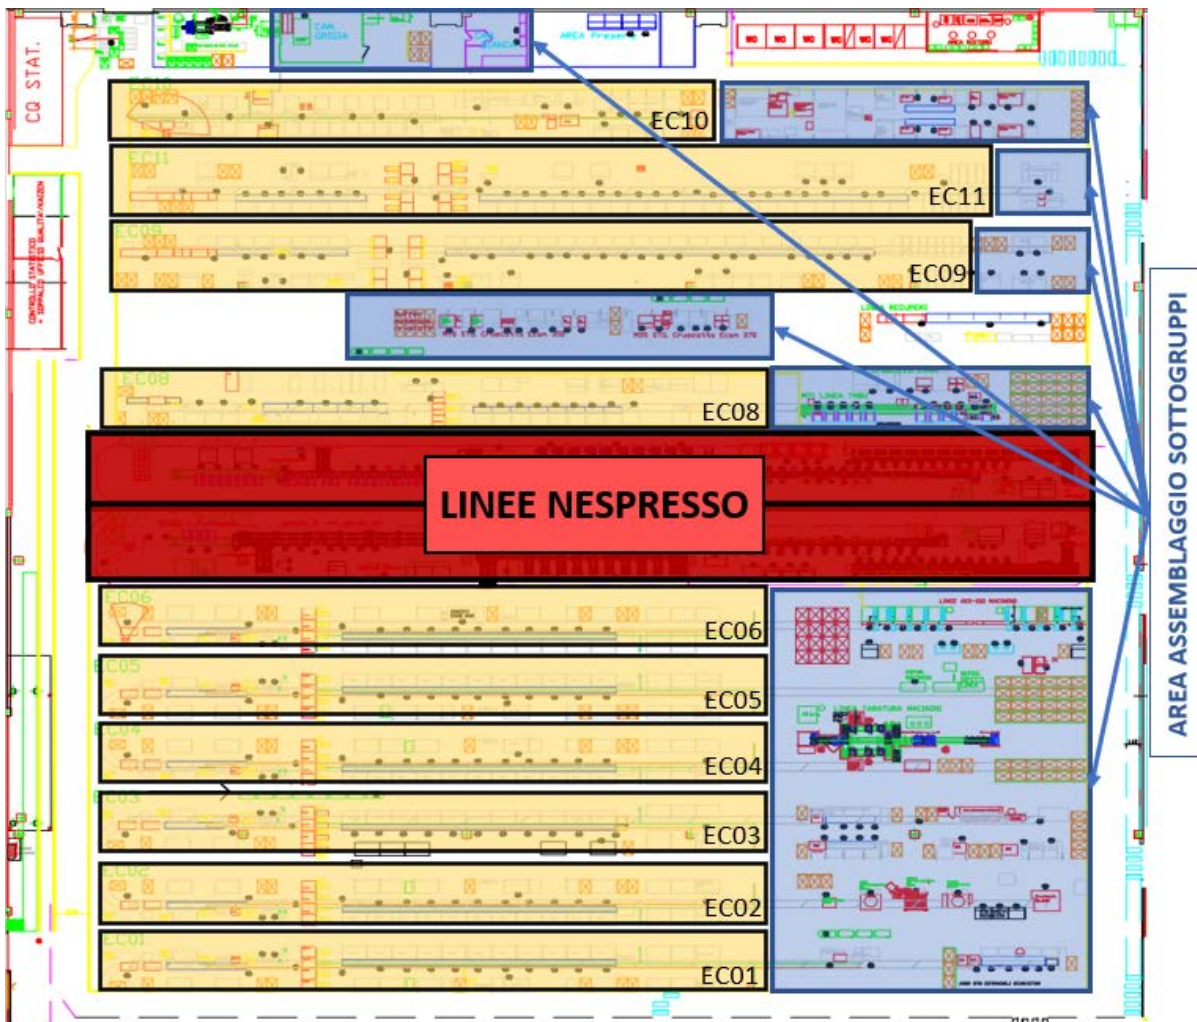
Layout del reparto assemblaggio dello stabilimento produttivo di Mignagola
